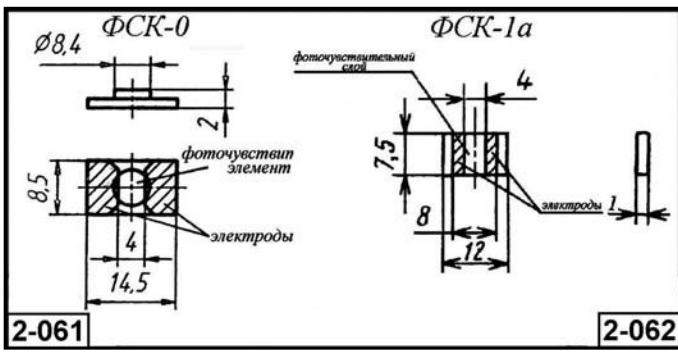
Внешний вид, габаритные размеры и ОСХ фоторезисторов на основе CdS
